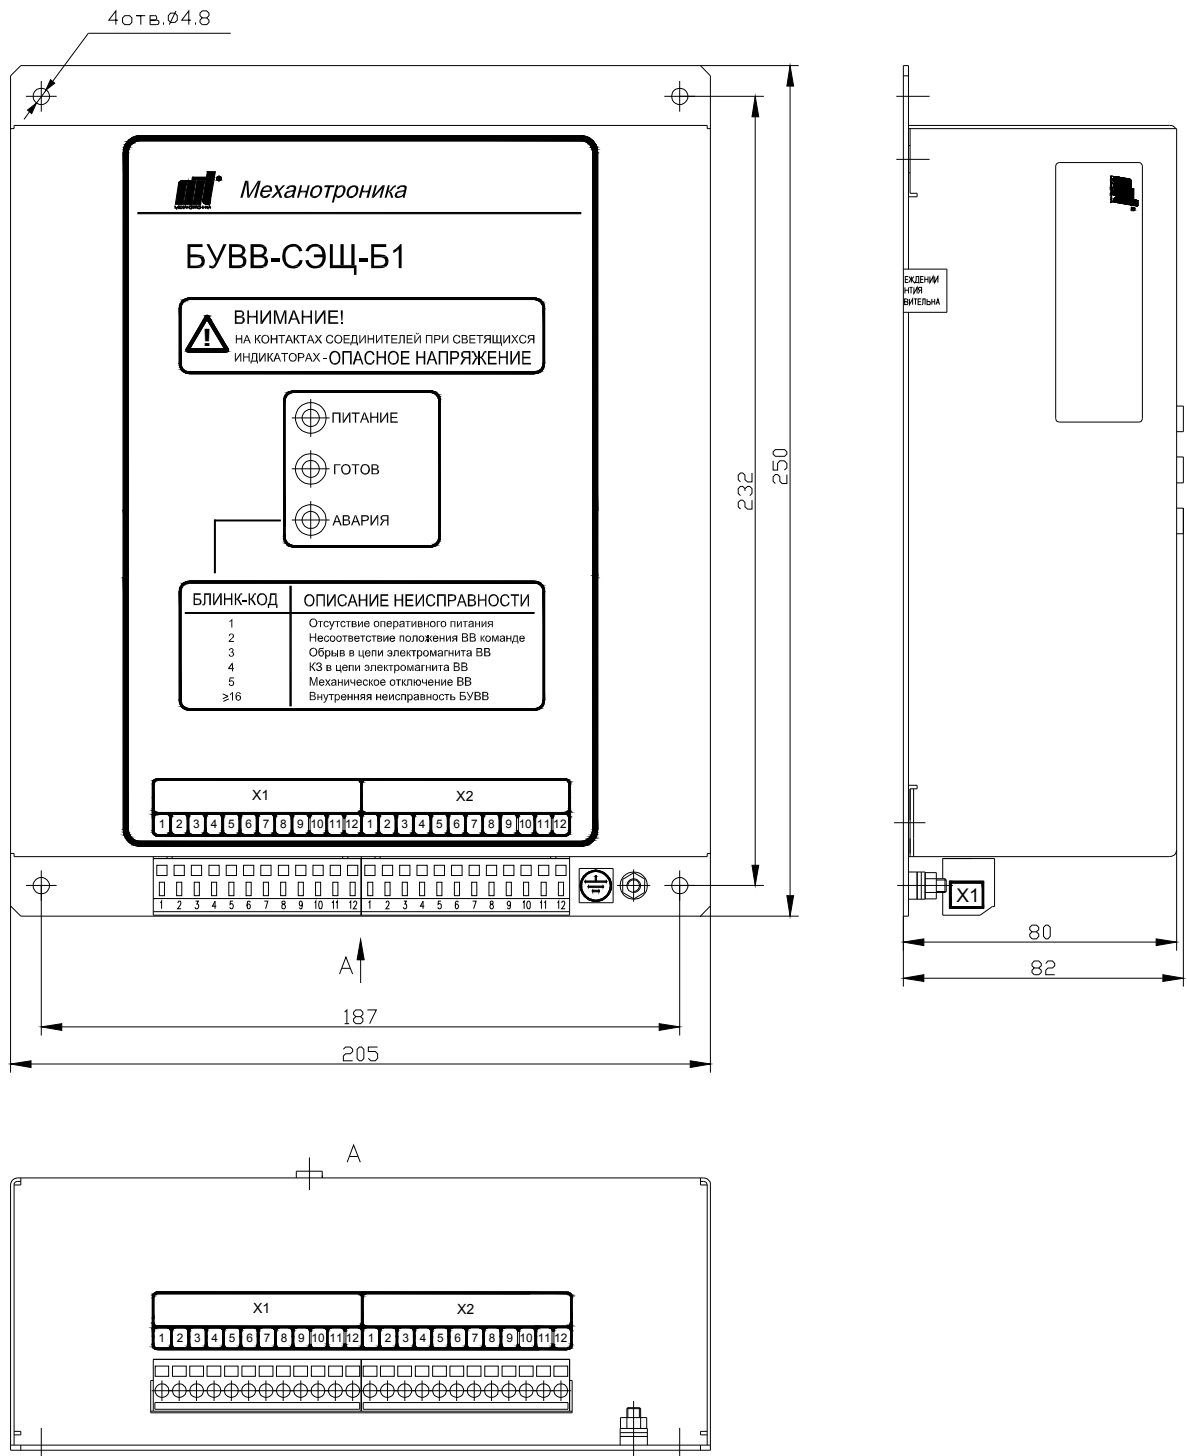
Вид блока ДИВГ.648228.101, габаритные и установочные размеры
